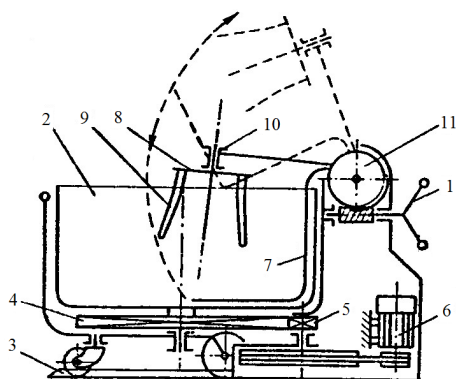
Schema malaxorului cu cuvă transportabilă; 1- manivelă; 2- cuvă; 3- placă fixare; 4- coroană dințată; 5- pinion; 6- electromotor; 7- braț fix; 8- disc; 9- lamele; 10- lagăr; 11- grup antrenare melc-roată melcată
